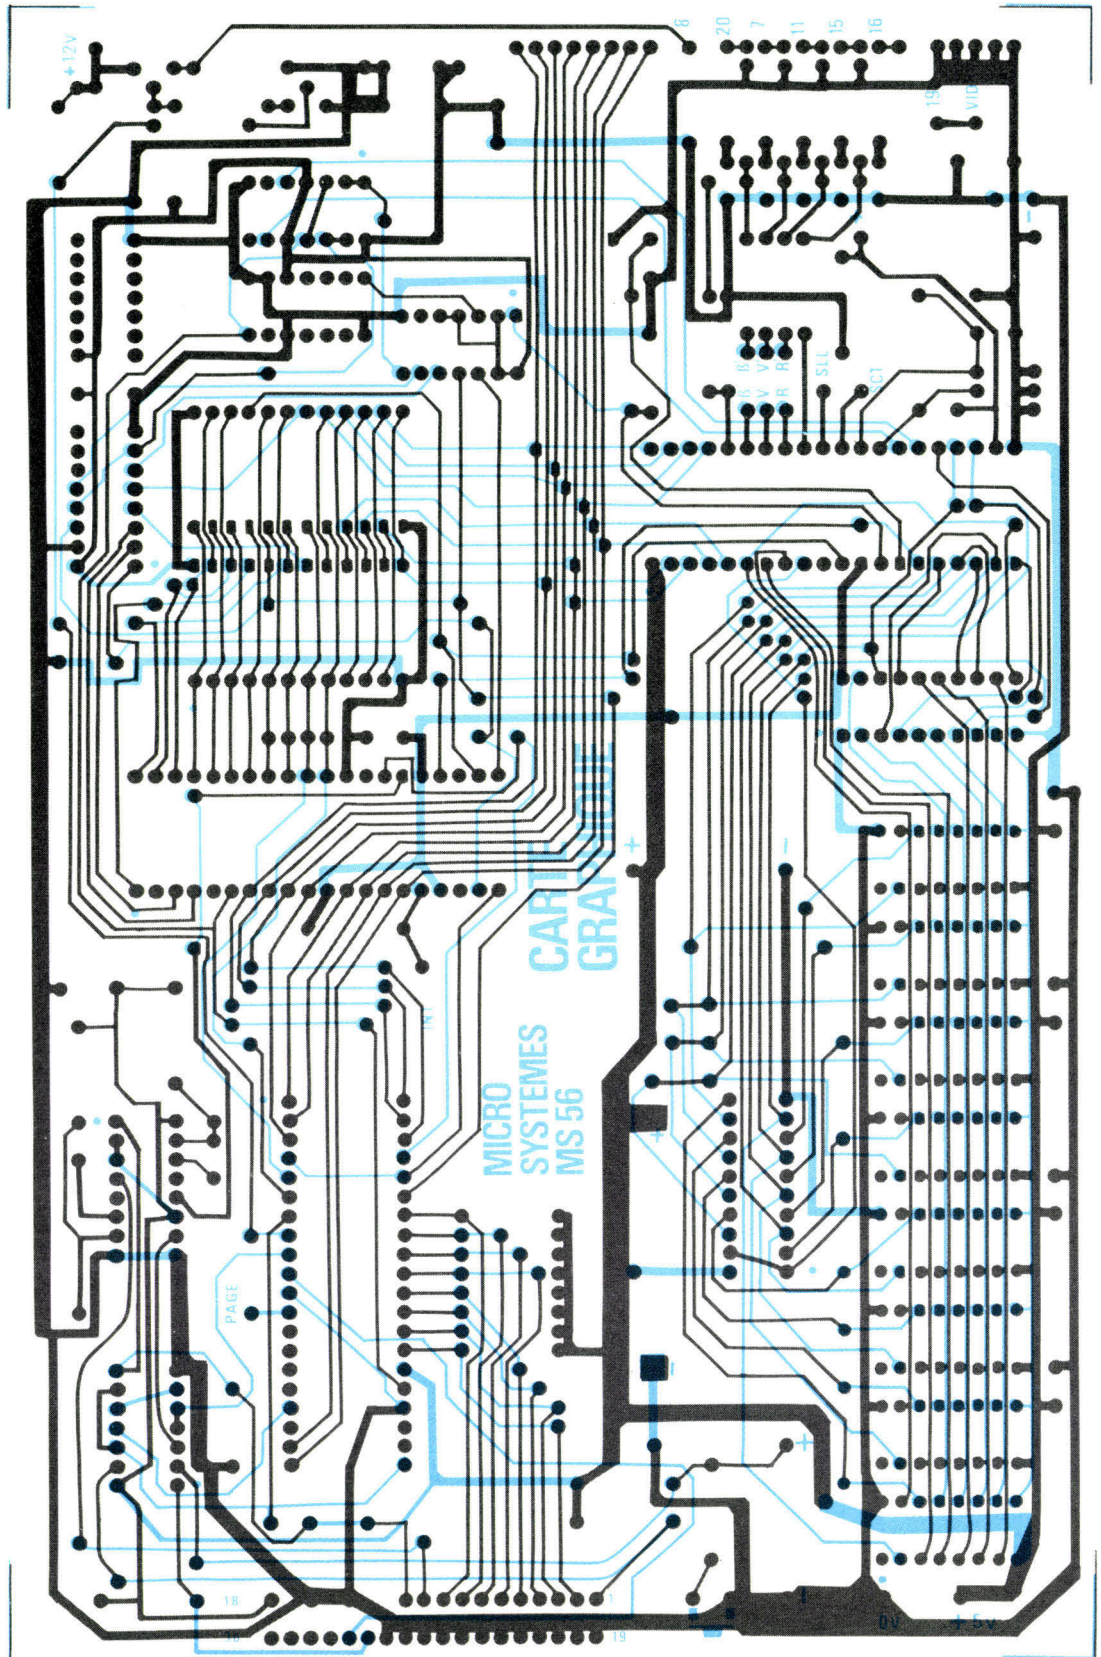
Circuit imprimé double face vu côté composants et côté soudures.
